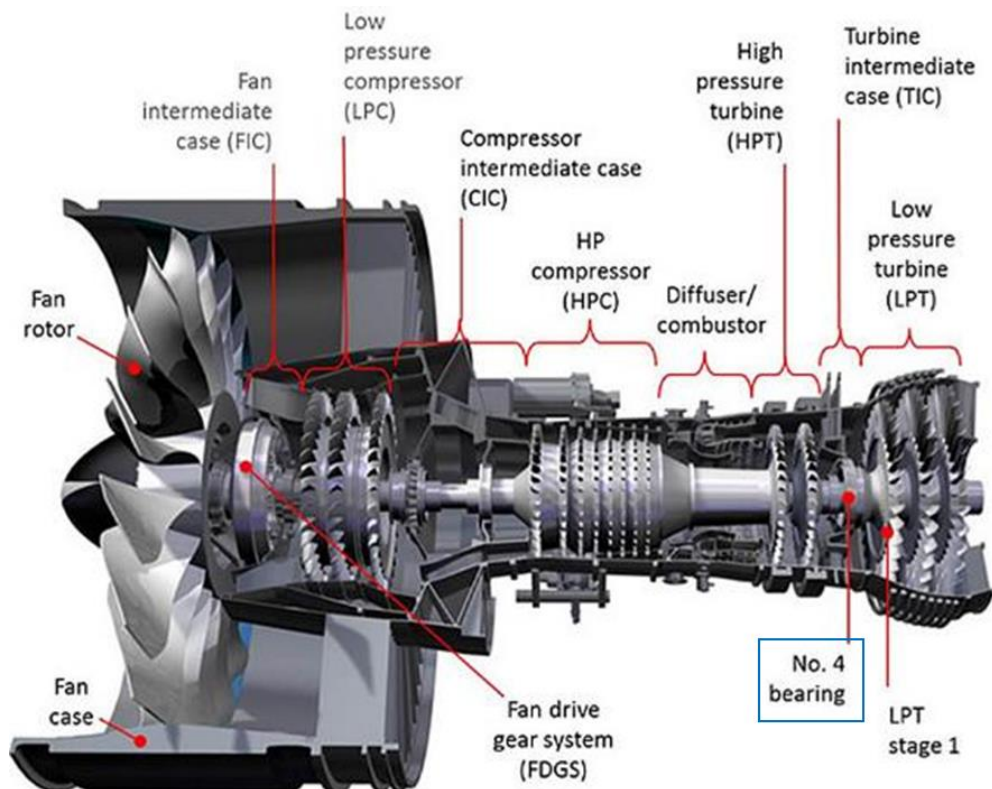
Vue de coupe d'un moteur PW1500 de Pratt & Whitney illustrant la position des systèmes clés d'une turbosoufflante (Bombardier Inc, 2014)
